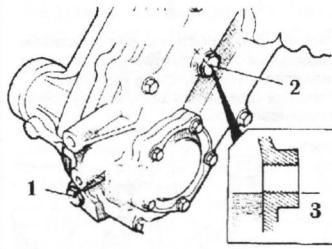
Местоположение заглушки передаточного кожуха
